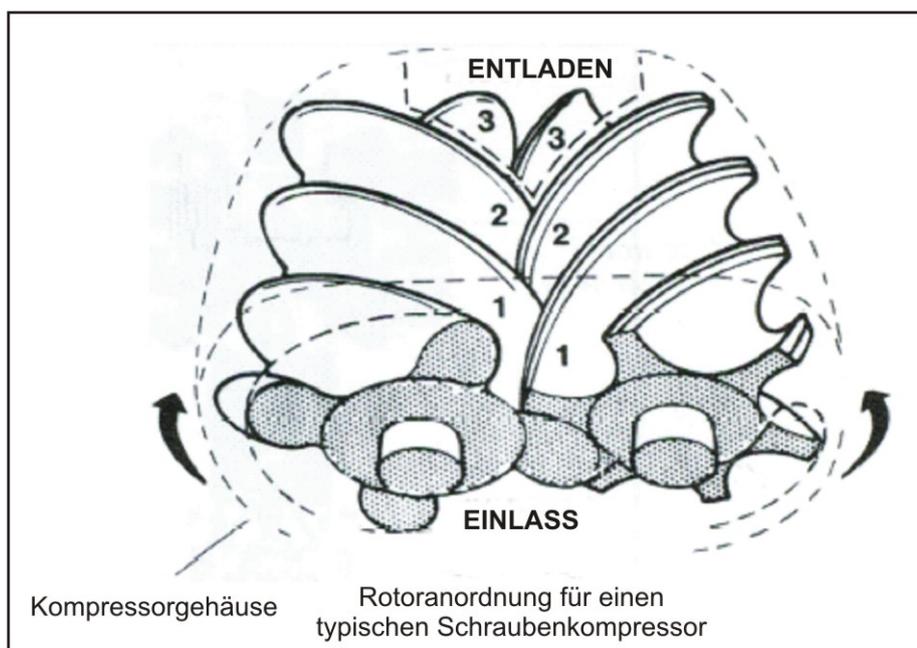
Typischer Rotor für einen ölfreien Schraubenkompressor
